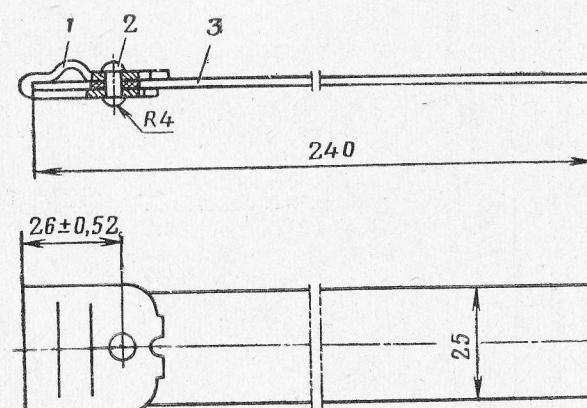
Ручка с наконечником для коробки под 7,62-мм винтовочные патроны:
